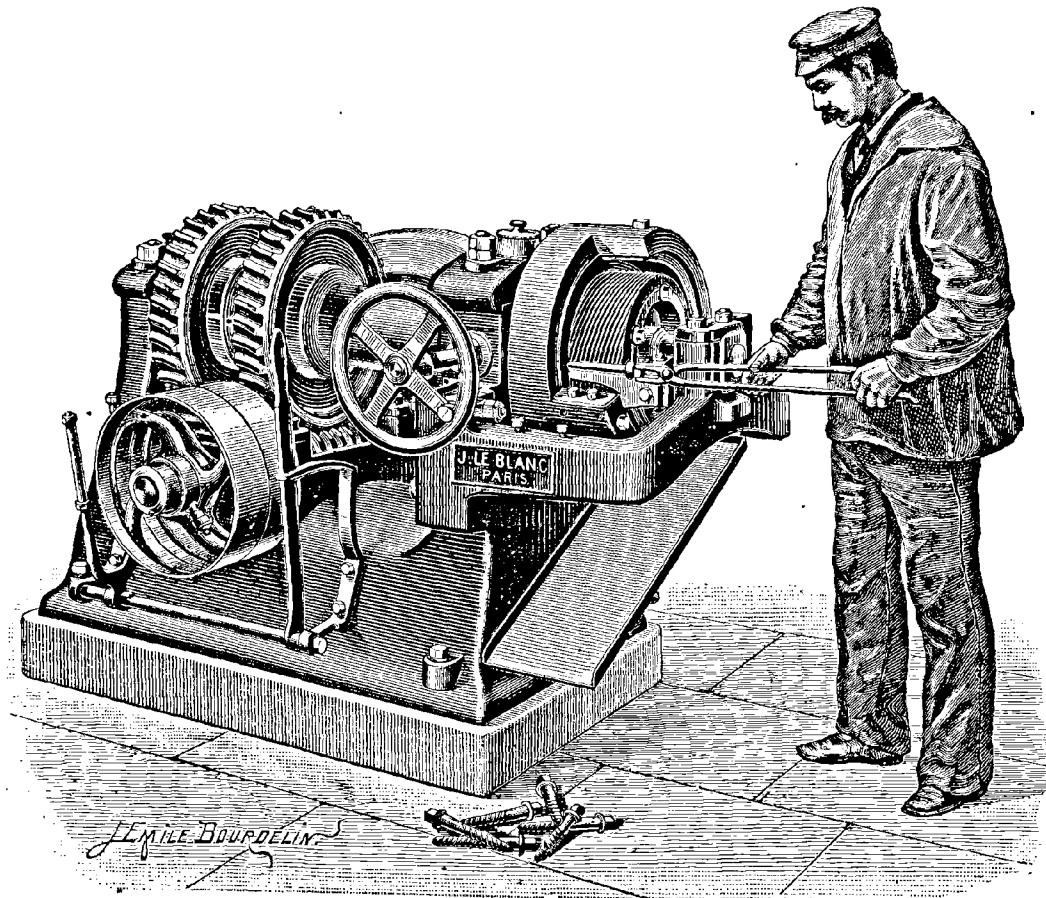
Machine à tarauder à chaud de M. Le Blanc.
